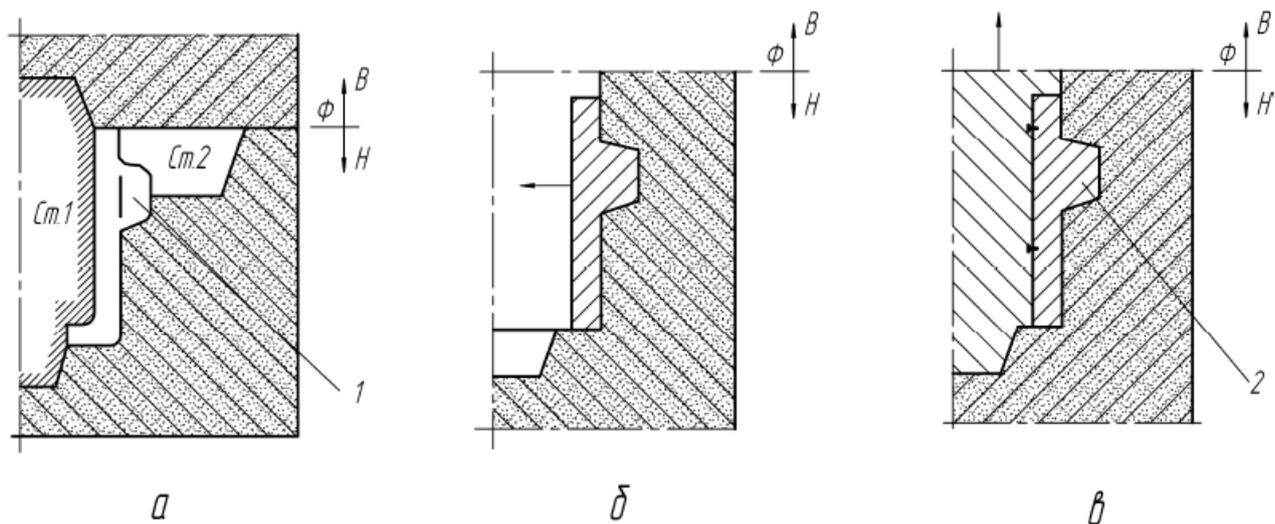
Элементы отливки, которые не извлекаются из отливки без разрушения формы
